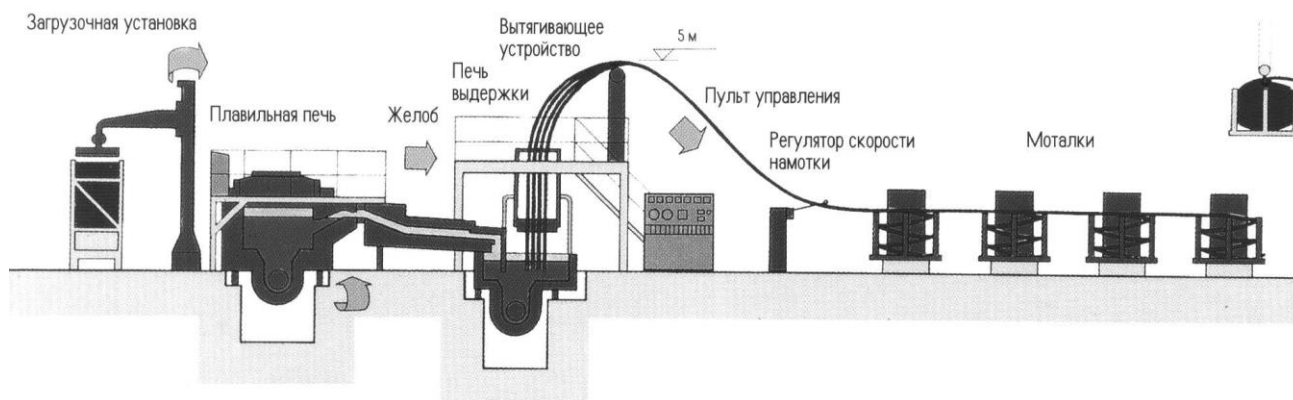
Установка непрерывного литья заготовок вертикально вверх фирмы Outokumpu
